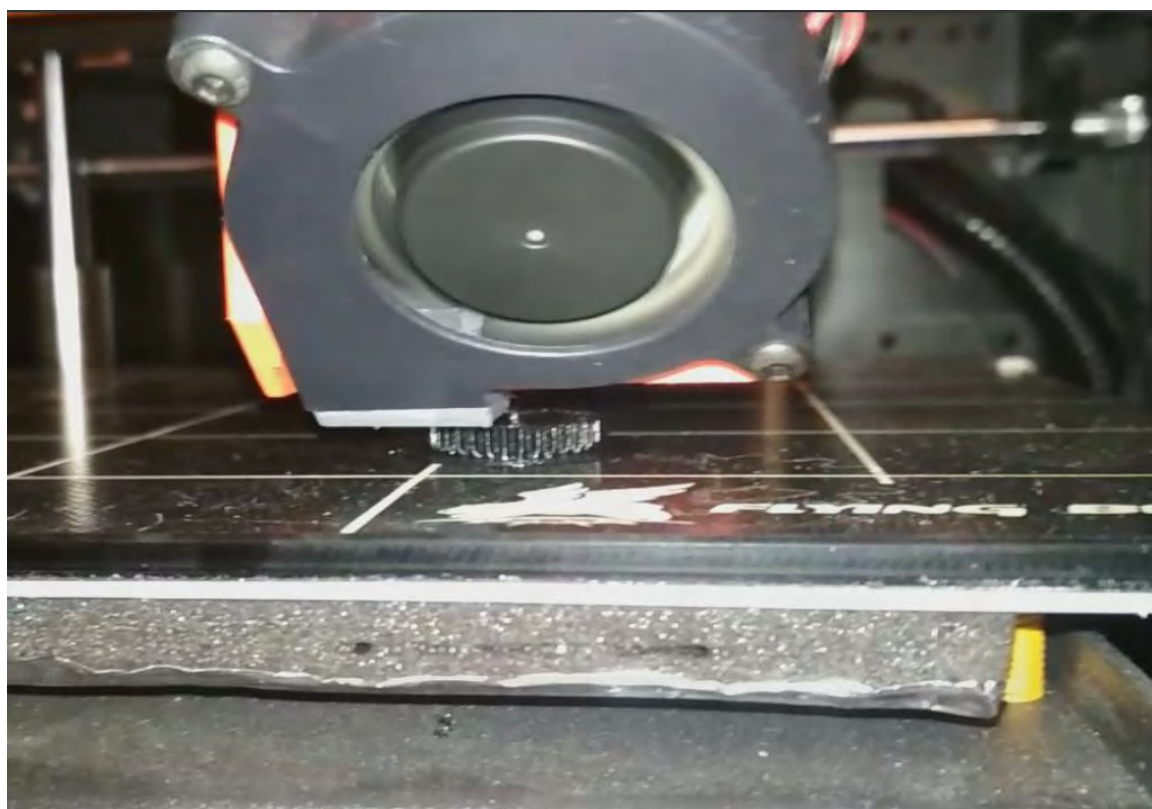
Процесс 3D-печати детали «Сателлит»
